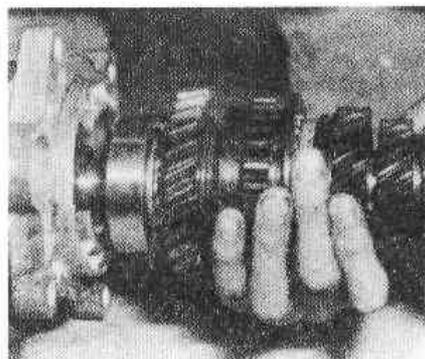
Установка стопорного кольца синхронизатора 3/4 передачи (Разд.6)
